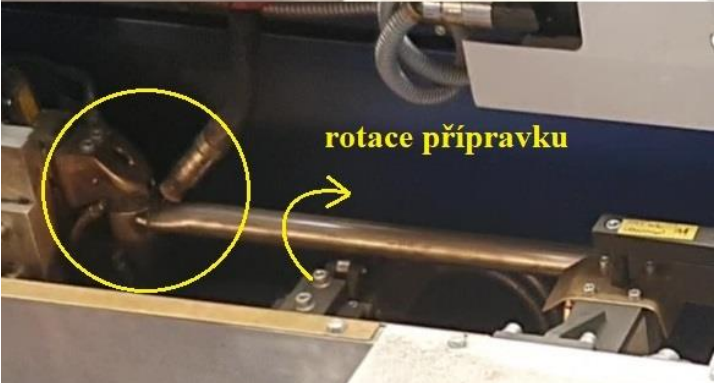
Rozdělení svařovacích parametrů po obvodu trubky – přípravek č. 1, levá strana
